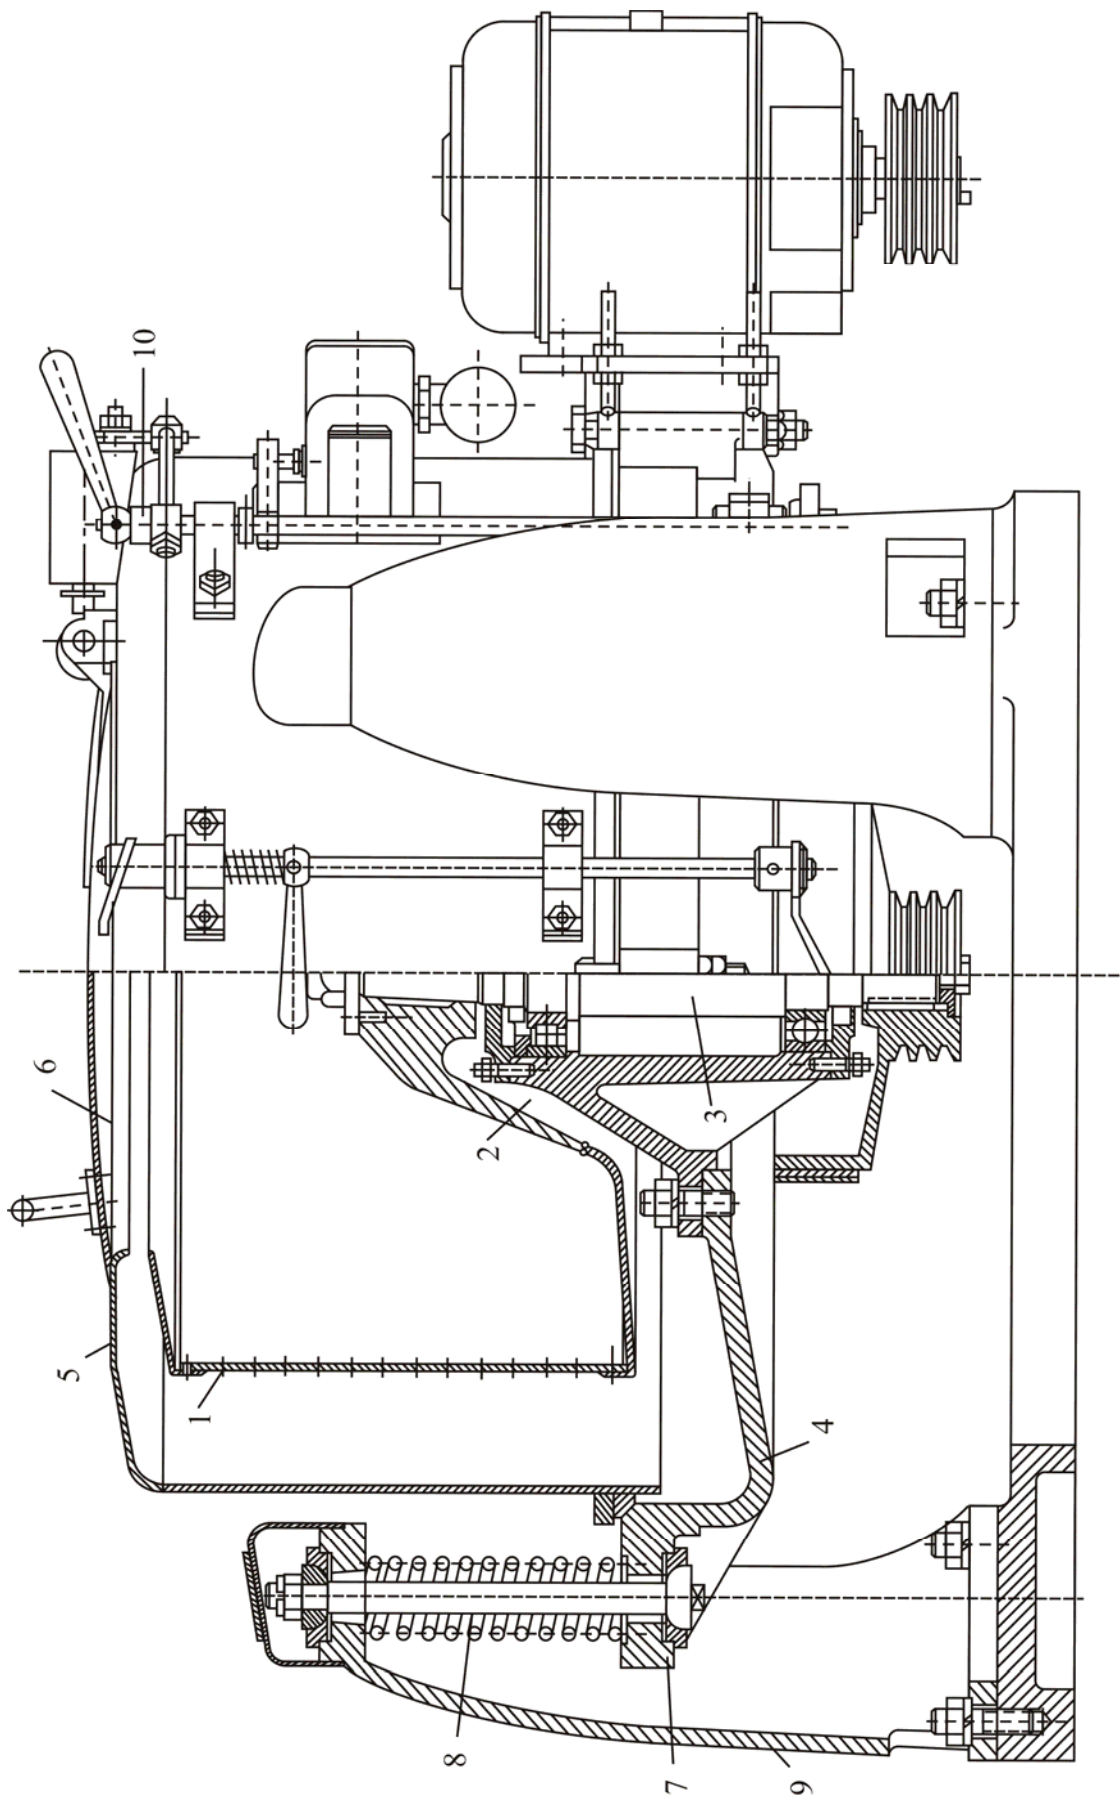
Трехколонная центрифуга: 1 – перфорированный ротор; 2 – опорный конус; 3 – вал; 4 – дно станины; 5 – неподвижный кожух; 6 – крышка кожуха; 7 – станина; 8 – тяга; 9 – колонка; 10 – ручной тормоз
